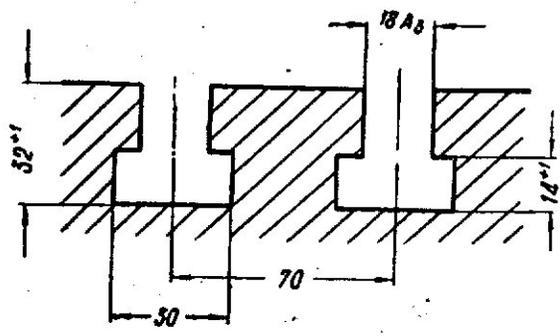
Эскиз Т-образных пазов станка модели 6М82Ш
